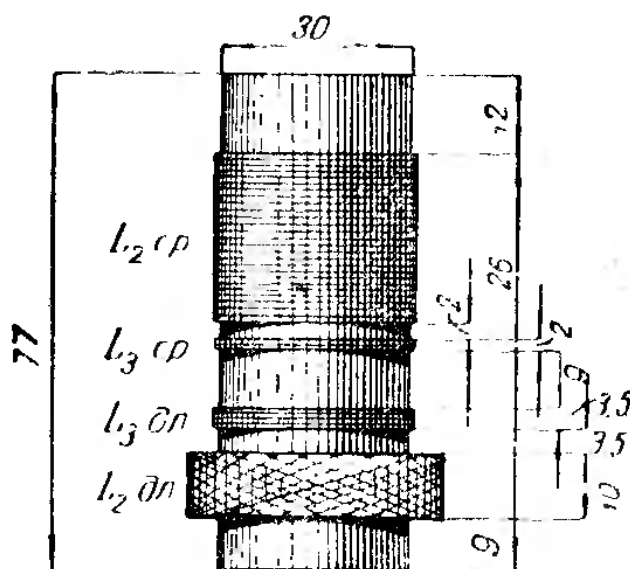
Расположение и основные размеры обмоток L_2 и L_3 катушки типа РФ-4.
